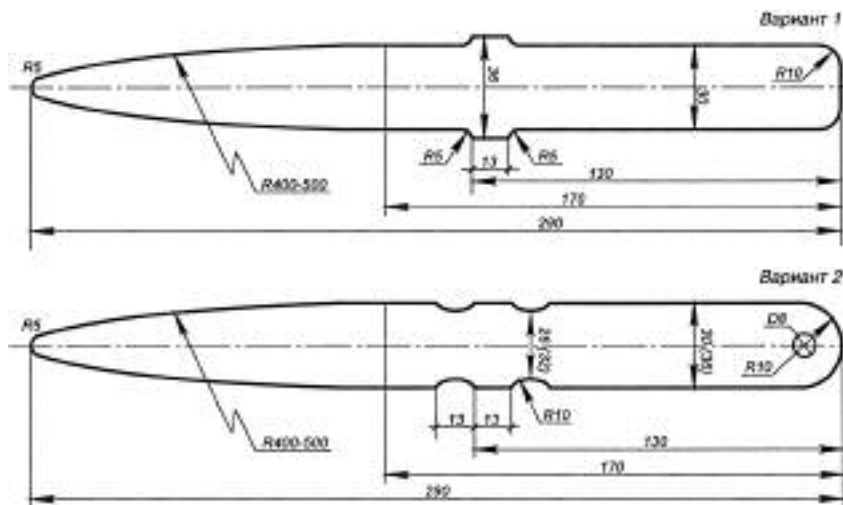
Нож спортивный метательный «Сибирский медведь-1»
